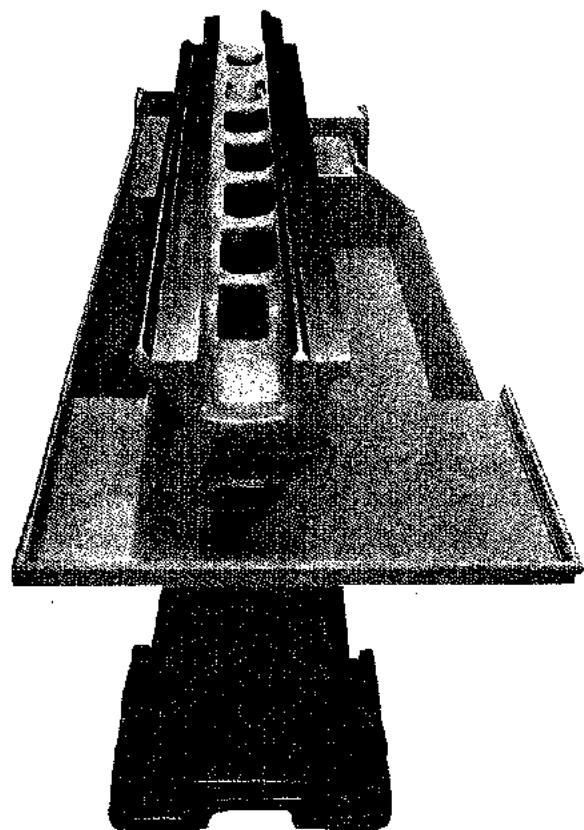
La bancada es la espina dorsal del torno (Monarch Machine Tool Co.).
